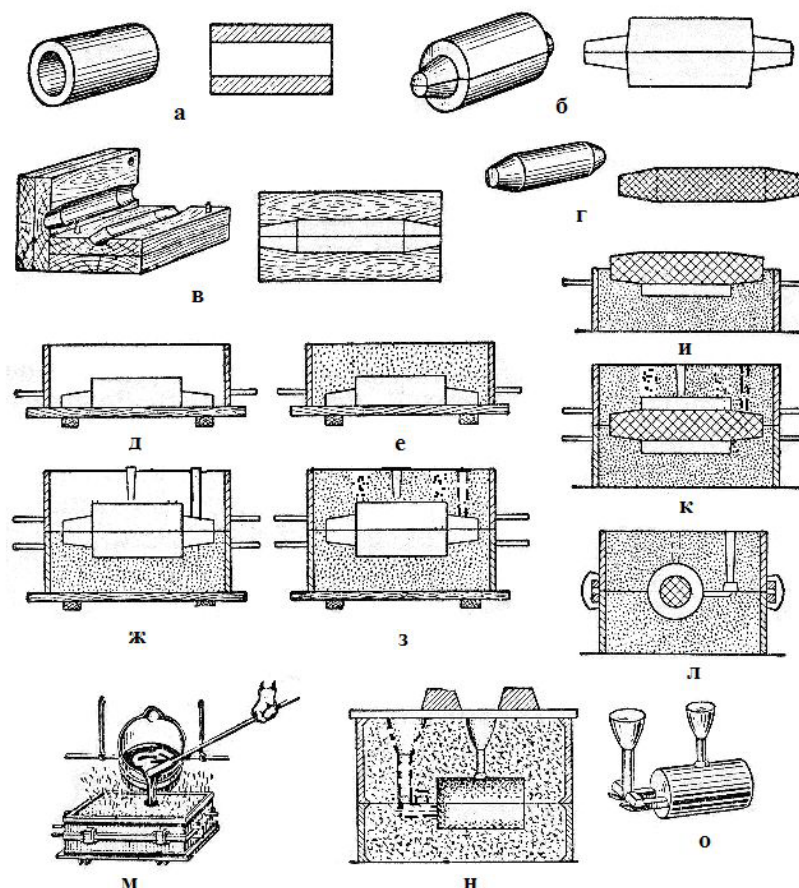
Процесс получения отливки в песчаной форме: а – отливка (штуцер); б – разъемная деревянная модель штуцера; в – стержневой ящик; г – стержень с коническими выступами по краям, устанавливаемый стержневым знаком; д – установка нижней половины модели в нижнюю опоку; е – формовка нижней опоки; ж – переворот нижней опоки, установка верхней половины модели и моделей литника и выпора (чаша сверху литника условно не показана); з – формовка верхней опоки; и – снятие верхней полуформы и установка стержня в нижнюю полуформу в специальные углубления (стержневые знаки); к – сборка формы; л – скрепление собранной формы; м – заливка в форму металла; н – литник и выпор в литейной форме; о – литниковая система и выпор в отливке
